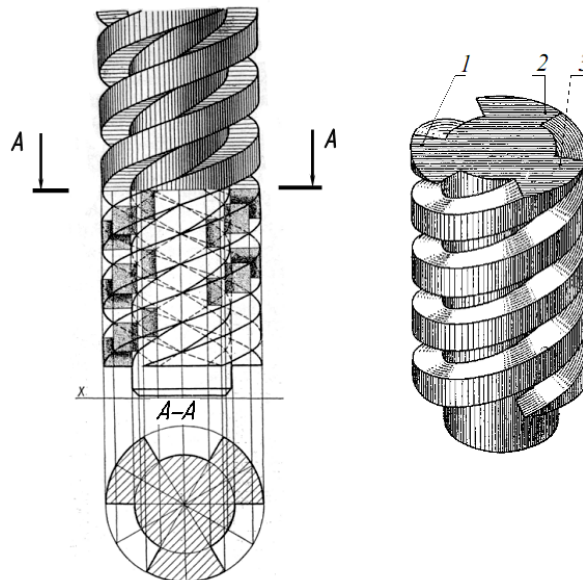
Трехзаходный винт с резьбой прямоугольного профиля
